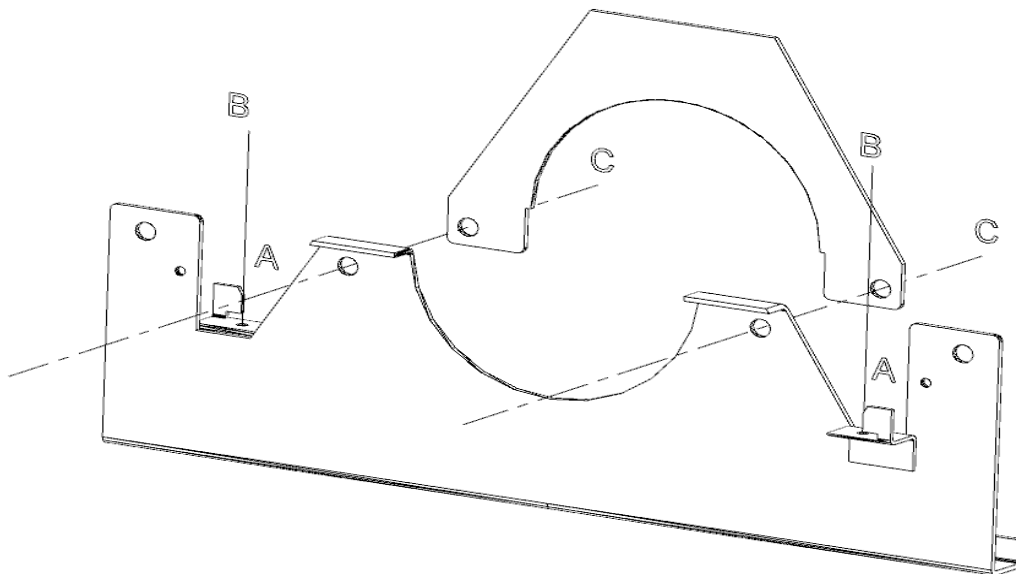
Кронштейн для крепления излучателя SBT в версии "I".
